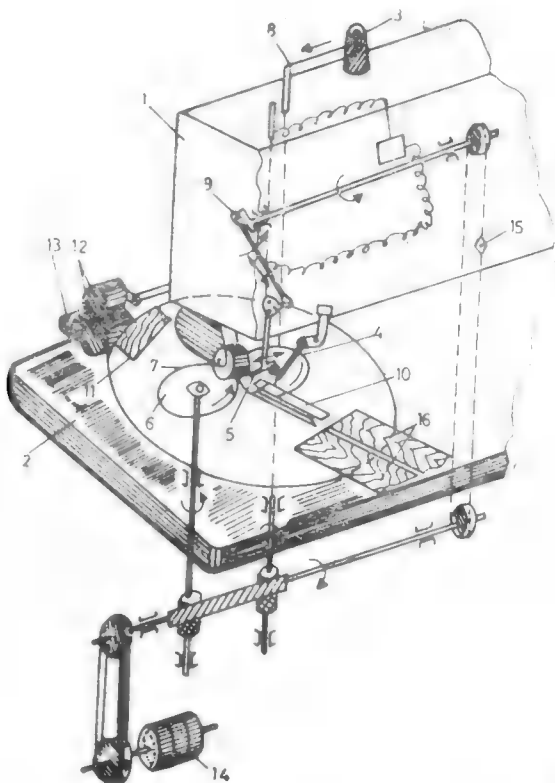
Mașina de îmbinat furnire, cu fir fuzibil.
